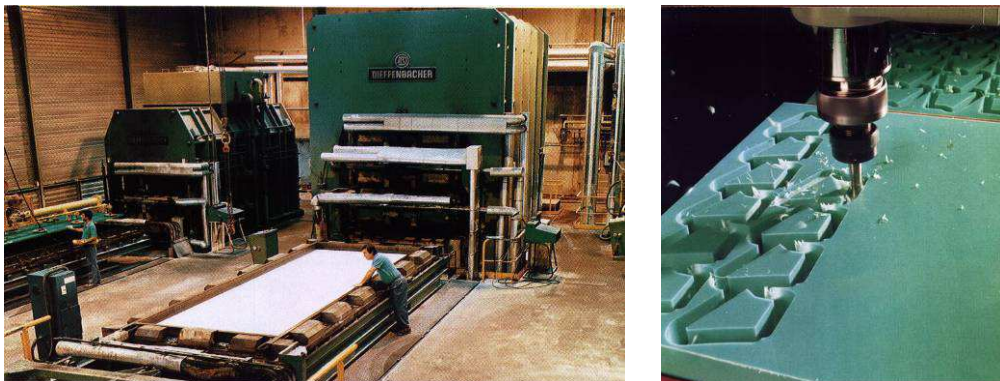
Moldagem e usinagem das placas. (Fonte: Catálogo Braskem S/A, 2008)
